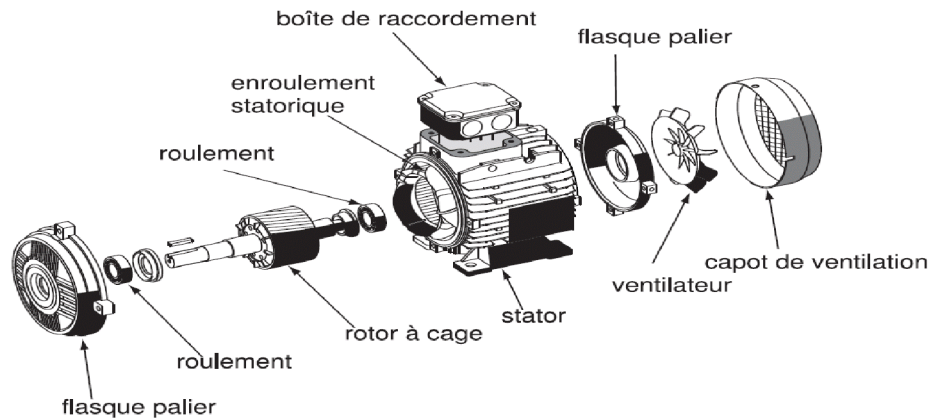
Vue détaillée d'une machine asynchrone à cage d'écureuil.
